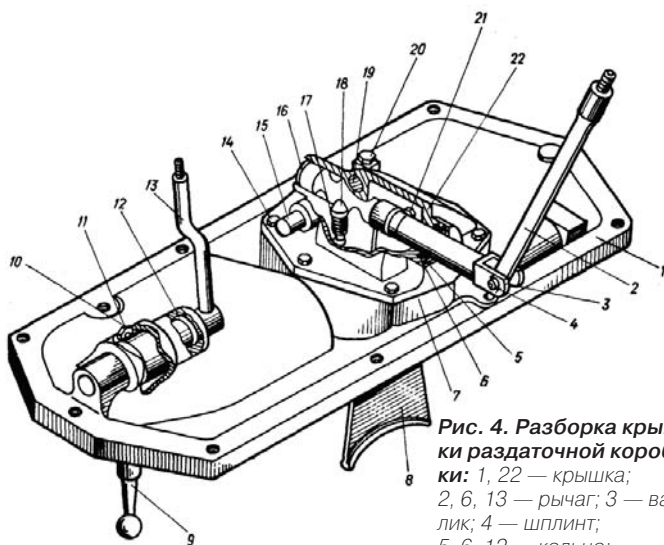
Разборка крышки раздаточной коробки: 1, 22 — крышка; 2, 6, 13 — рычаг; 3 — валик; 4 — шплинт; 5, 6, 12 — кольцо;
